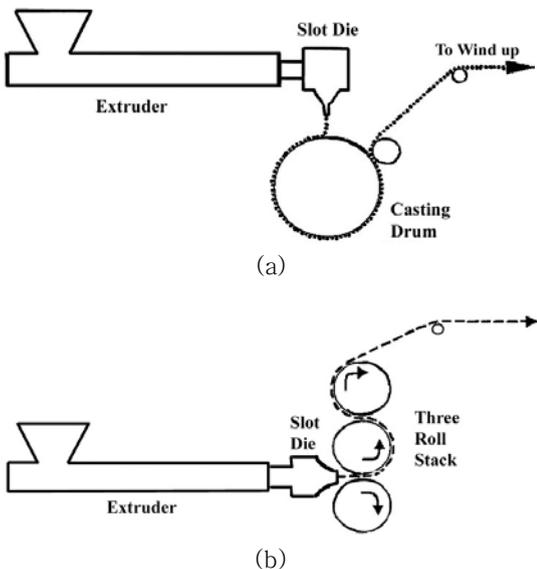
PEEK 필름 및 시트 주형 장치. (a) casting drum and (b) three-roll stack.
